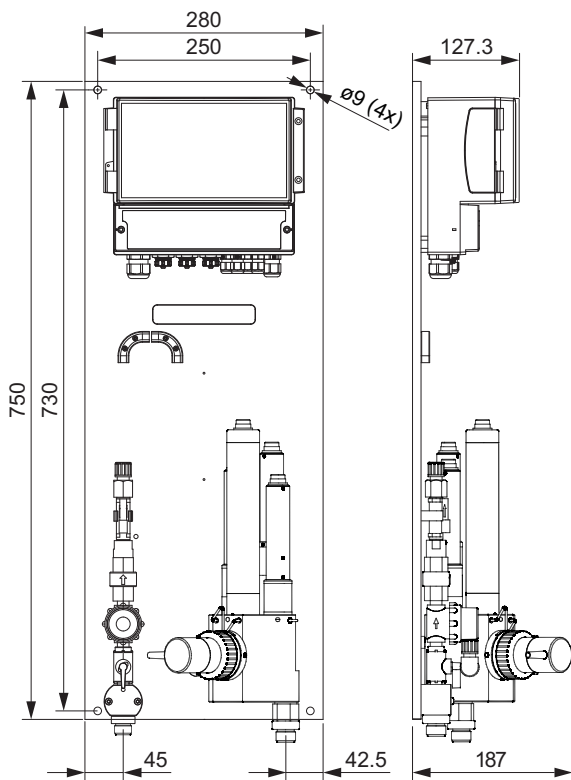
Abmessungen (in mm) des DID mit Durchflusszelle, Installationsausführung BT4 für bis zu drei Sensoren plus einen Sensor
